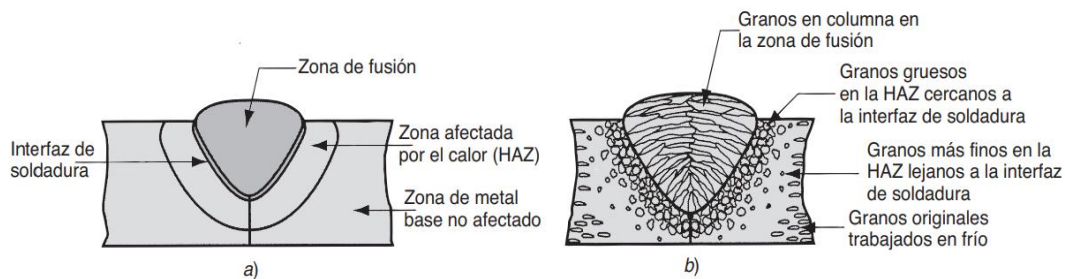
Zonas afectadas por proceso de soldadura por fusión. Fundamentos de manufactura moderna (2007, p. 700). Mikell P.
